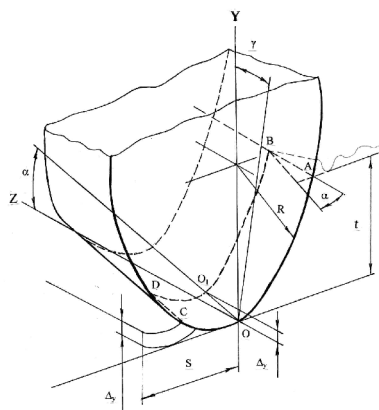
Номинальная площадь контакта детали и резца с неперетачиваемой круглой пластиной.
